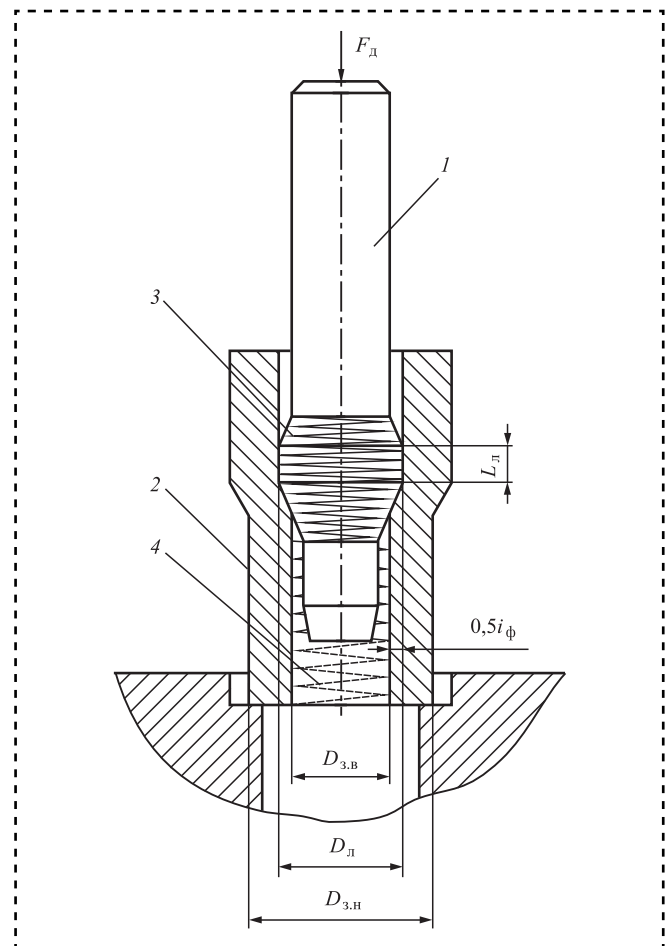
Схема дорнования отверстия полой цилиндрической заготовки:
